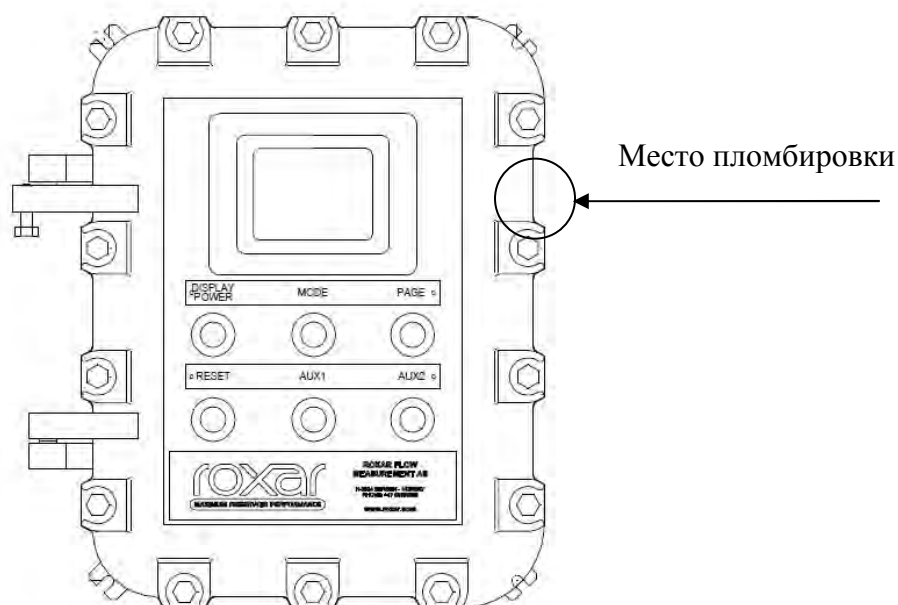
Схема пломбировки корпуса компьютера потока
